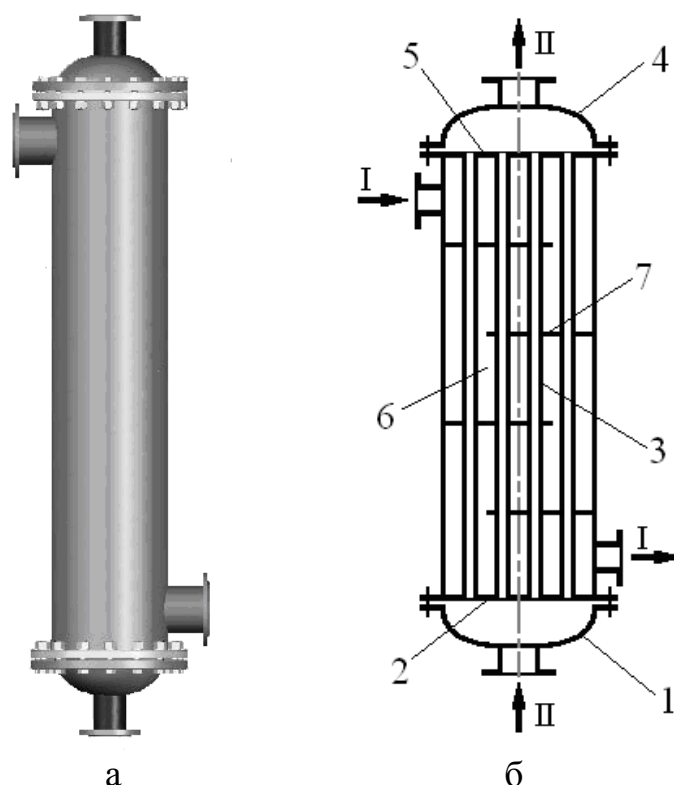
Кожухотрубчатый одноходовой теплообменник, внешний вид (а) и схема устройства (б):
